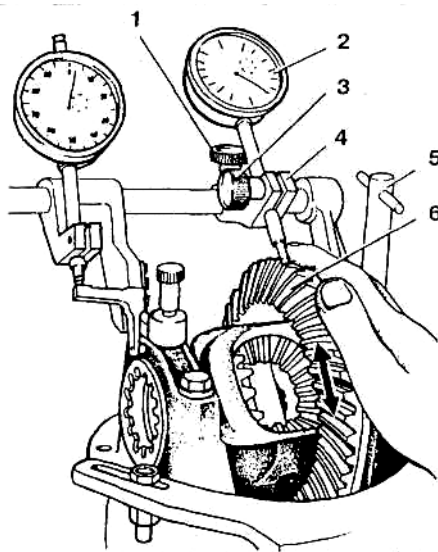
Проверка бокового зазора в зацеплении шестерен главной передачи приспособлением А.95688/Р:
